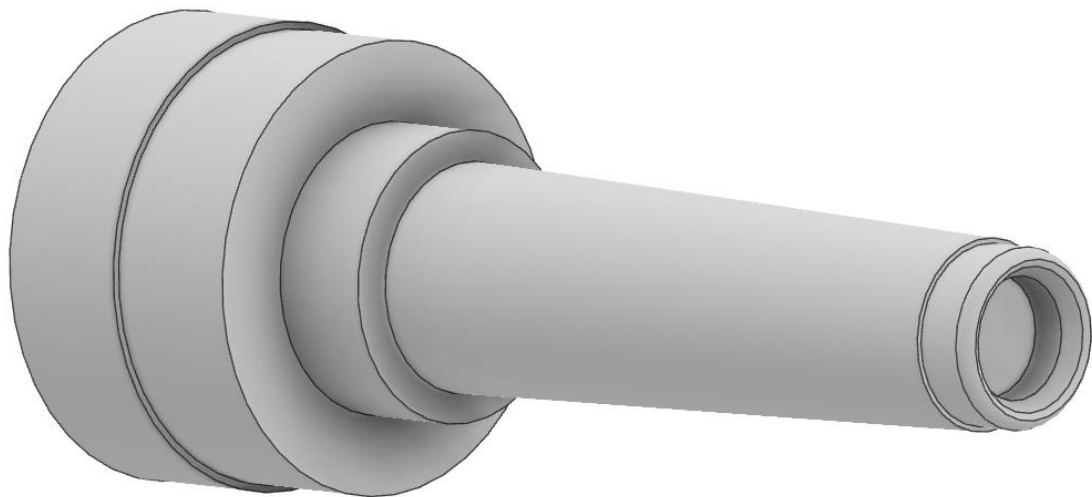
Результат обертання ескізу для формування тіла заготовки
